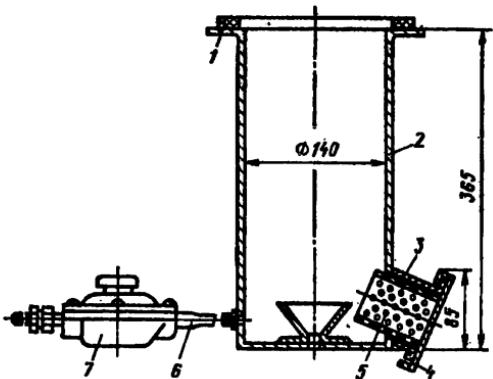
Заглушка для проверки герметичности впускного тракта:
